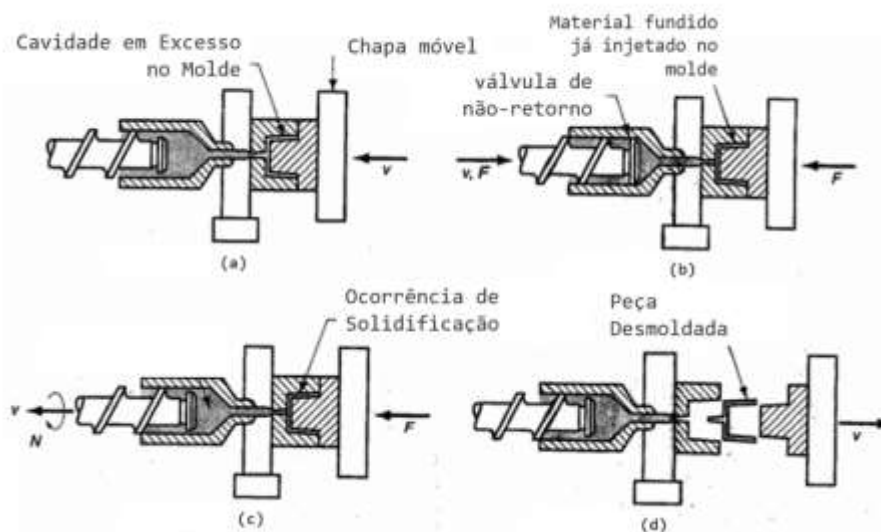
Processo de moldagem por injeção. Fonte: Mechanical Arena, com alterações
